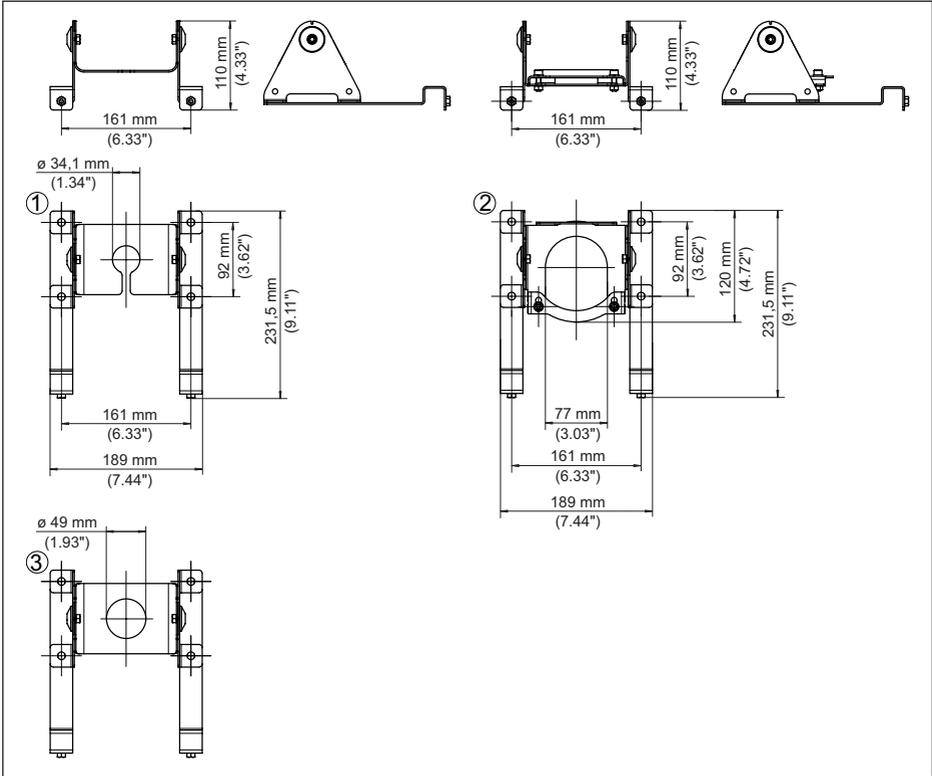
Montagebügel für Kunststoffbehälter - mit Fixierung für IBC-Behälter
